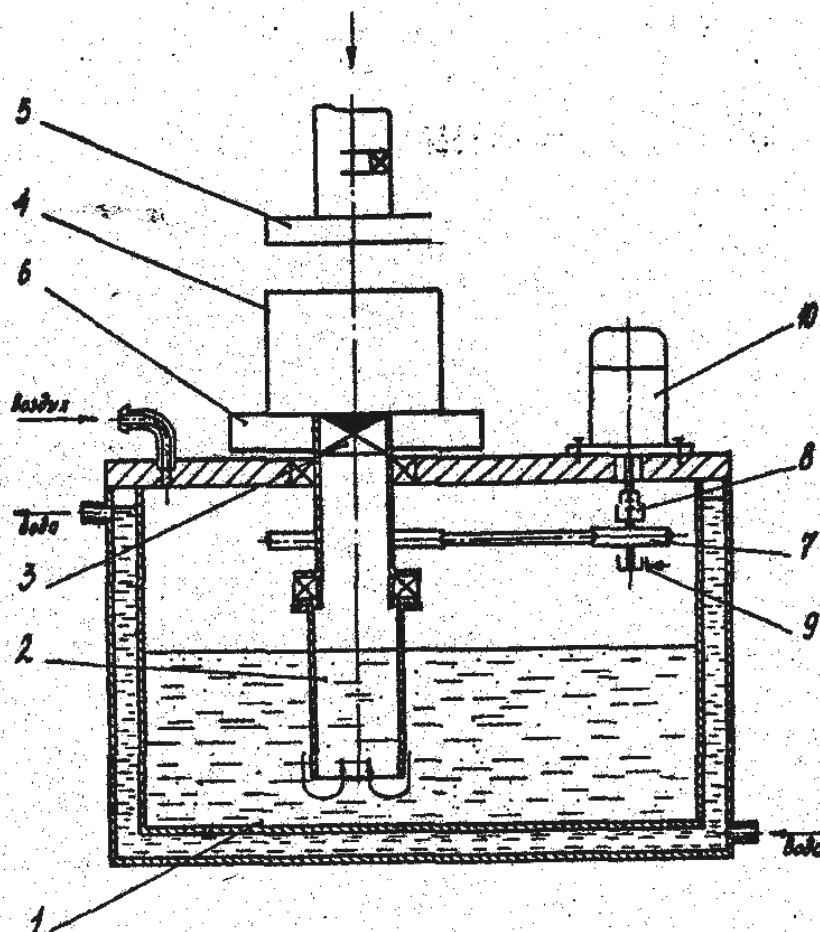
Устройство для центробежного литья с подпрессовкой
